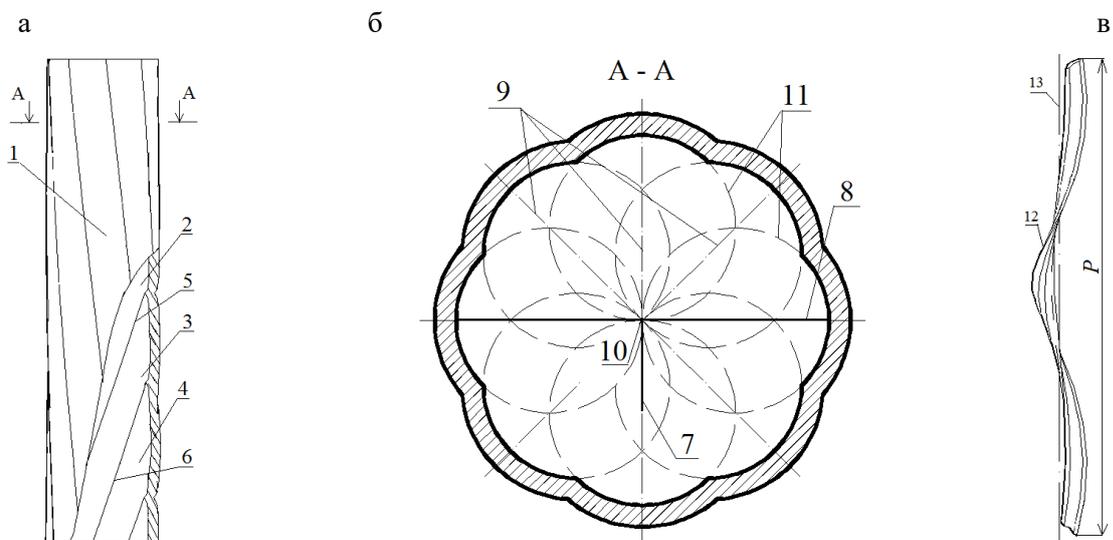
Завихритель для закручивания потока (заявка на патент RU №2018118240): а – общий вид устройства; б – разрез А-А; в - продольный разрез образующего корпуса желоба
